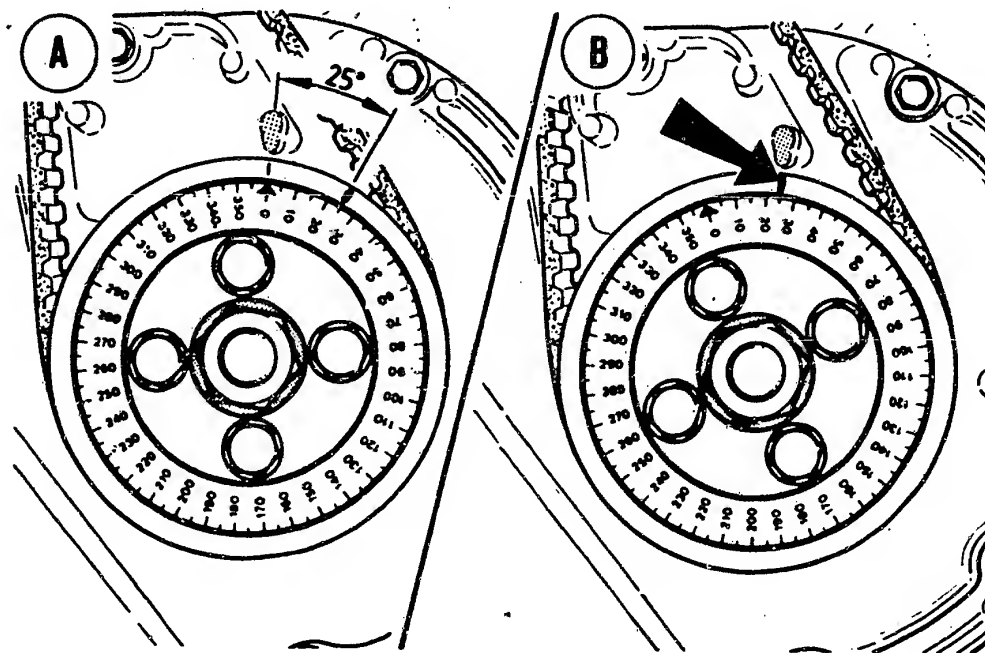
Diesel-Motor: Bild A zeigt die OT-Position des 1. Zylinders anhand einer Gradskala auf dem Einspritzpumpenrad. In B ist ersichtlich, dass die Markierungen 25° früher übereinstimmen.
